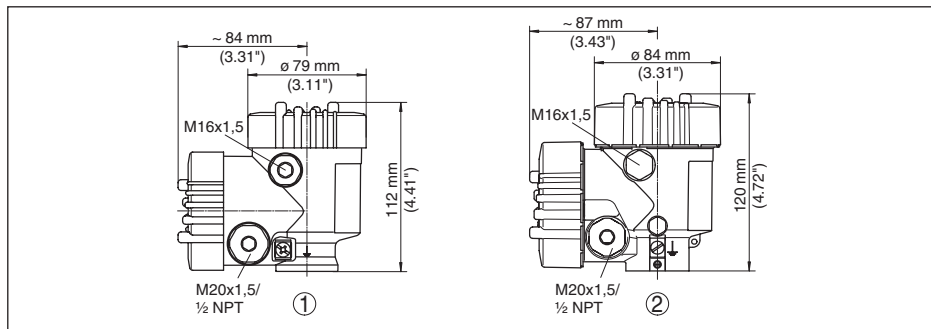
Размеры корпуса - с установленным модулем индикации и настройки корпус выше на 9 мм (0.35 in)
